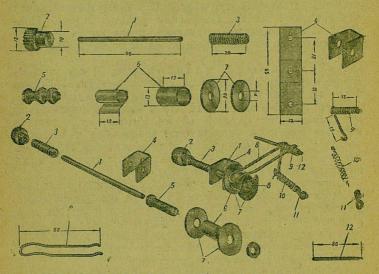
Лентопротяжный механизм: I—ось от «конструктора», 2— шестеренка от «конструктора» для связи с червяком электромотора, 3— распорная втулка, 4— подшипник, 5— гнездо от радиоприемника, 6— бумажная гильза протягивающего валика, 7— картонные шеки валика, 8— петля, 9— спиральная втулка прижимной пружины, 10—оттяжная пружина, 11—крючок оттяжной пружины, 12— ось спиральной части 9 оттяжной пружины.
